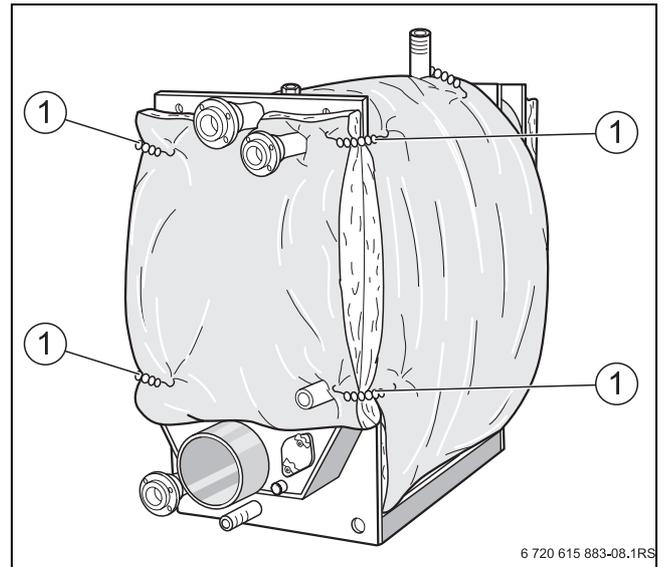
Размещение и крепление теплоизоляции задней стенки
